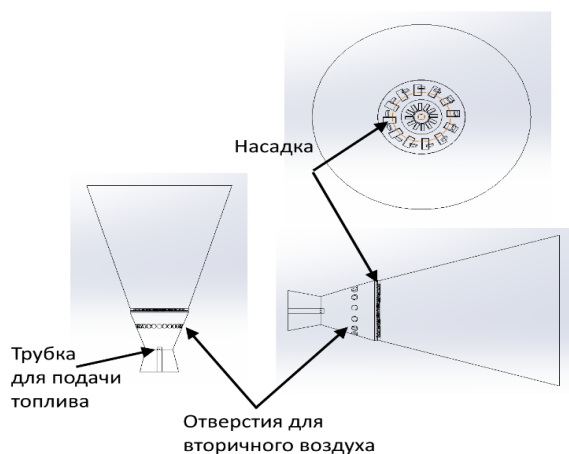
Продольный, поперечный и трехмерный вид горелочного устройства
